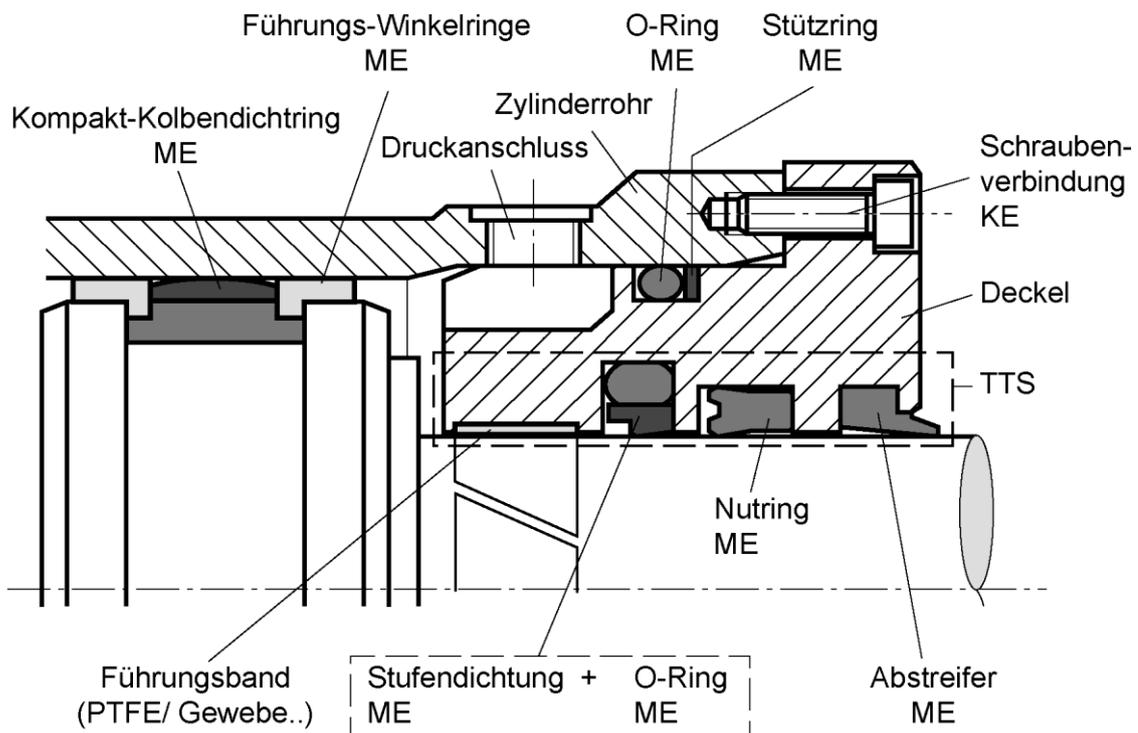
Ein Hydraulikzylinder als technisches System – Dichtungen und Führungen (TTS – Technisches Teilsystem [Baugruppe, Funktionseinheit], KE – Konstruktionselement, ME - Maschinenelement)
